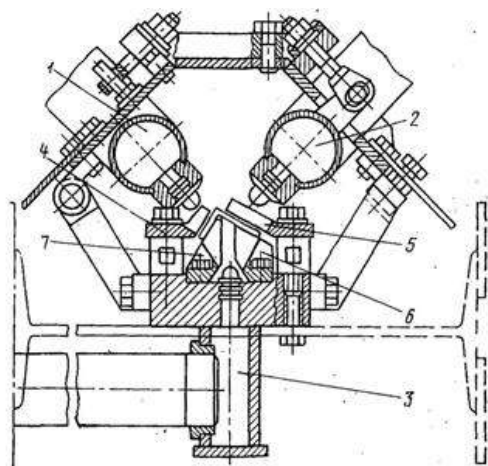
Схема струевого устройства для охлаждения неравнополочного уголка конструкции УкрНИИМет: 1, 2, 3 – коллектора; 4, 5, 6, 7 – направляющие
